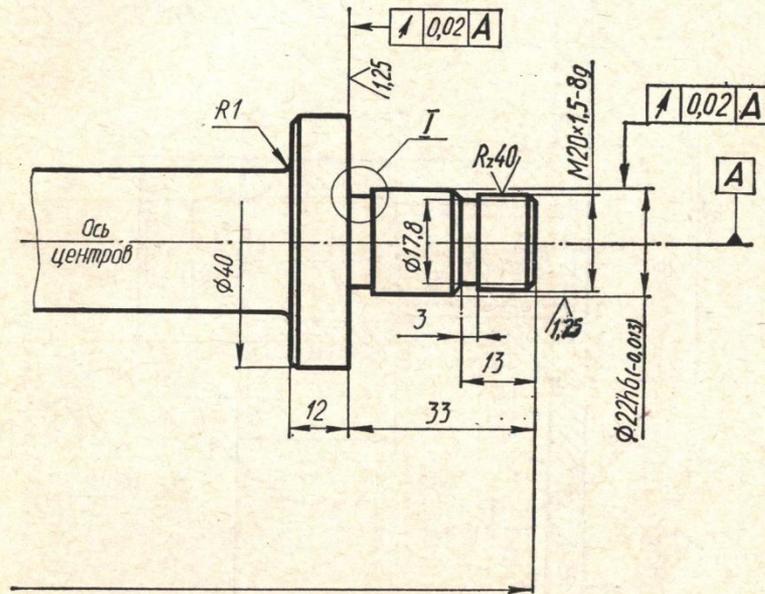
Условные обозначения допусков расположения и формы на чертежах:
